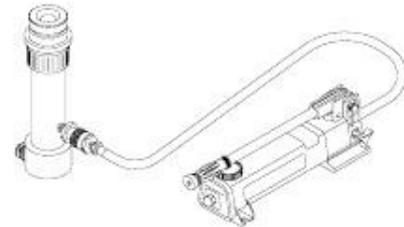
10-t-Hydraulikzylinder mit Pumpe
